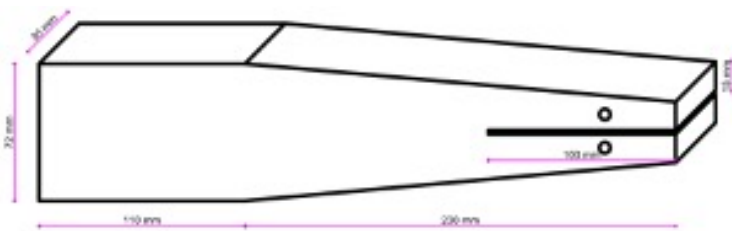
Eprouvettes pour l'essai de fissuration
